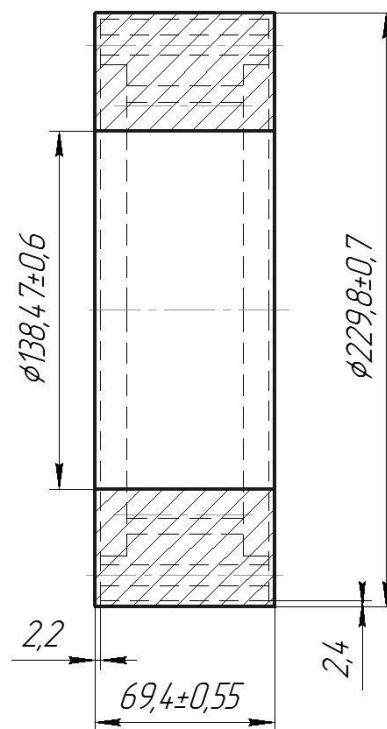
Ескіз заготовки виливок отриманий методом відцентрового ЛИТТЯ
